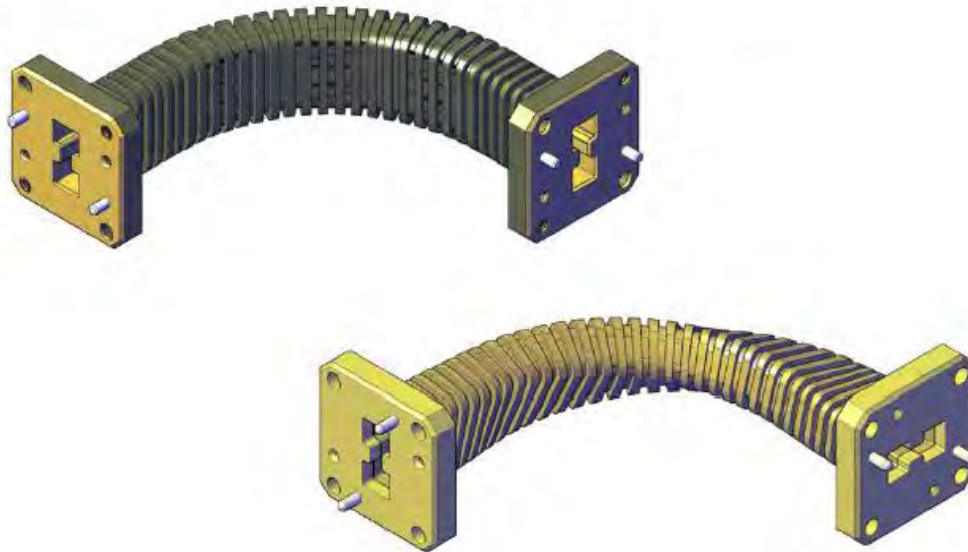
Розміри і електричні параметри гофрованого хвилеводу (від фірми Space Machine and Engineering)
